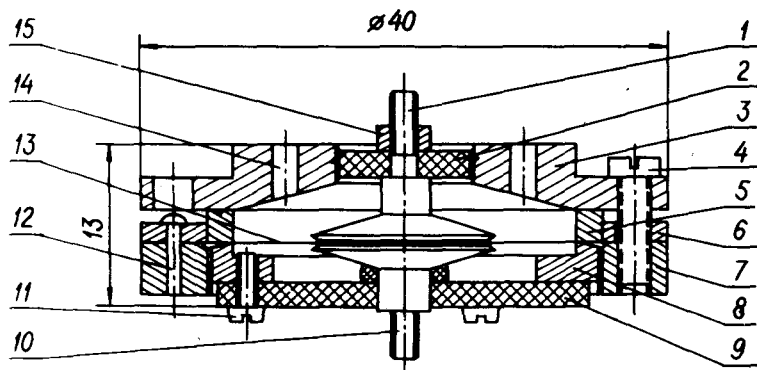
Схематический разрез ДК-79 (без вакуумируемого корпуса).
